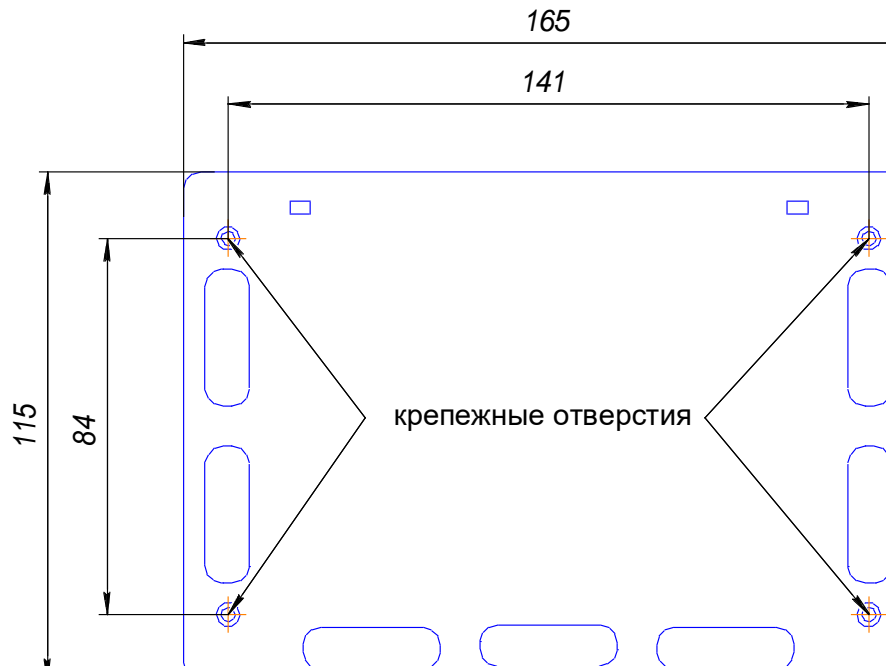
а. Разметка крепления АКШ ФИДШ.426461.001 в пластмассовом корпусе
